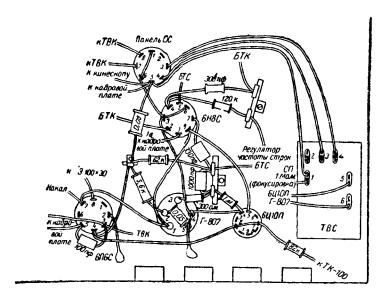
Монтажная схема блока разверток телевизора КВН-49 при переделке для кинескопа 35ЛК2Б.
